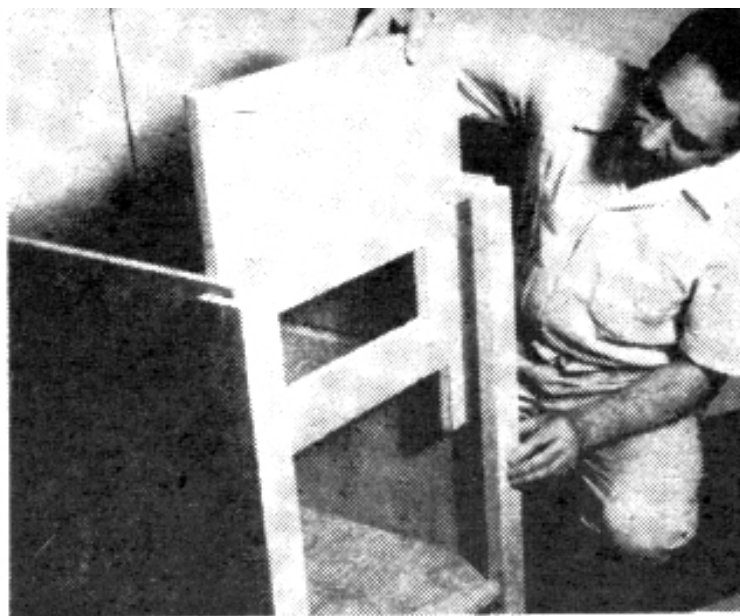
Corte el panel del sintonizador amplificador por la plantilla del fabricante.
